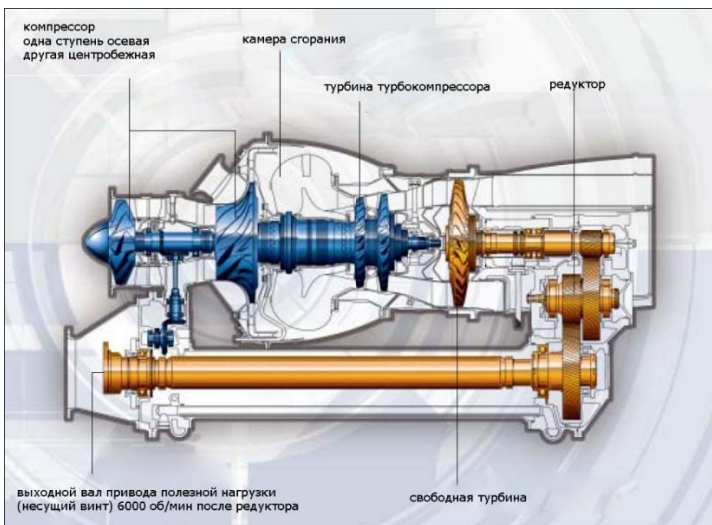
Схема двигателя Turbomeca Arriel с промежуточным редуктором
